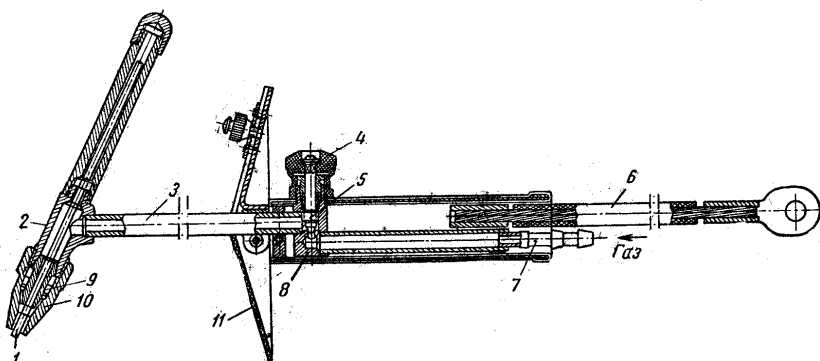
Горелка для ручной аргоно-дуговой сварки вольфрамовым электродом
